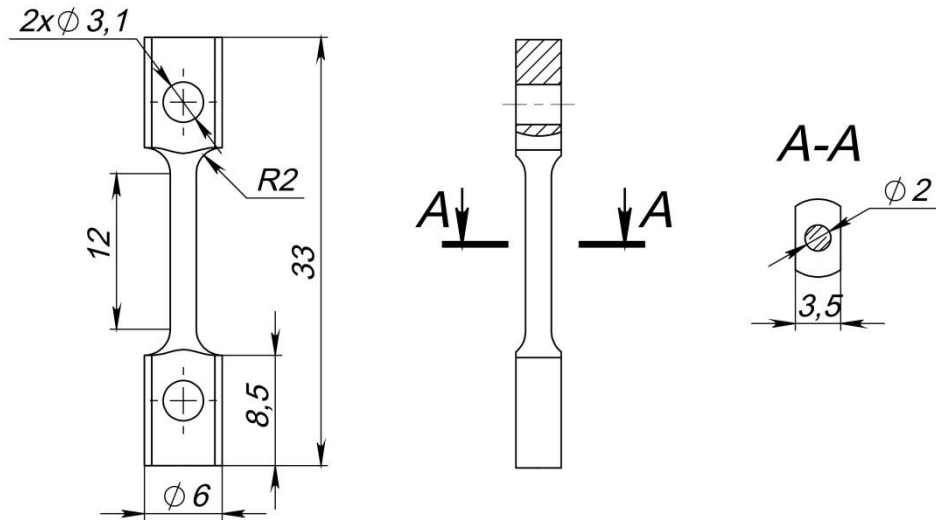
Образец для автоклавных испытаний на коррозионное растрескивание под напряжением
